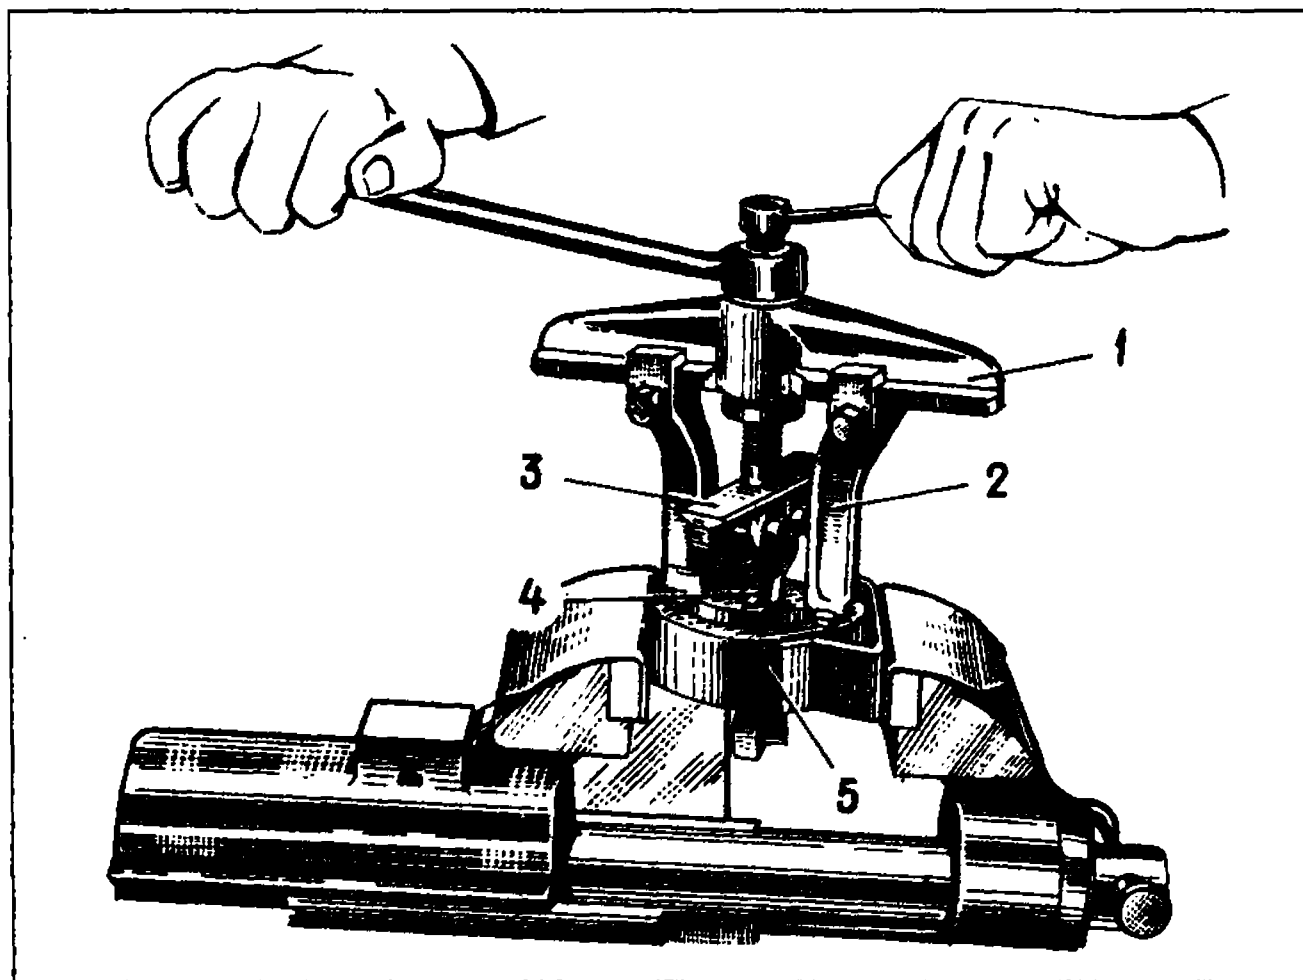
Выпрессовка подшипника из упругой опоры:
